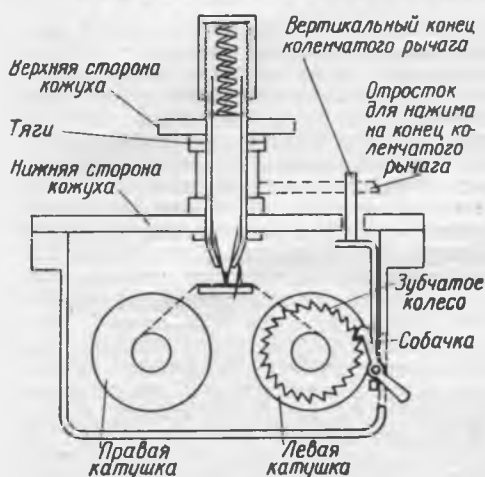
Поперечный разрез обоймы карандаша и коробки.
